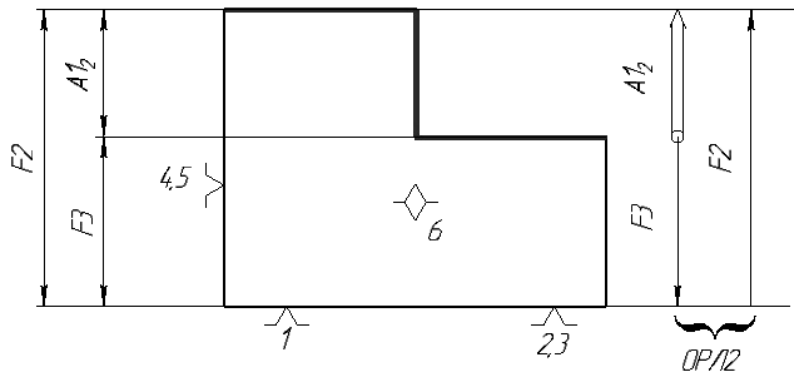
Операційний ескіз оброблення деталі фрезеруванням (варіант 2)
